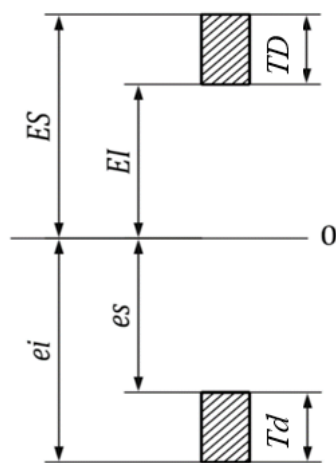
Схема розташування полів допусків посадок з зазором.
